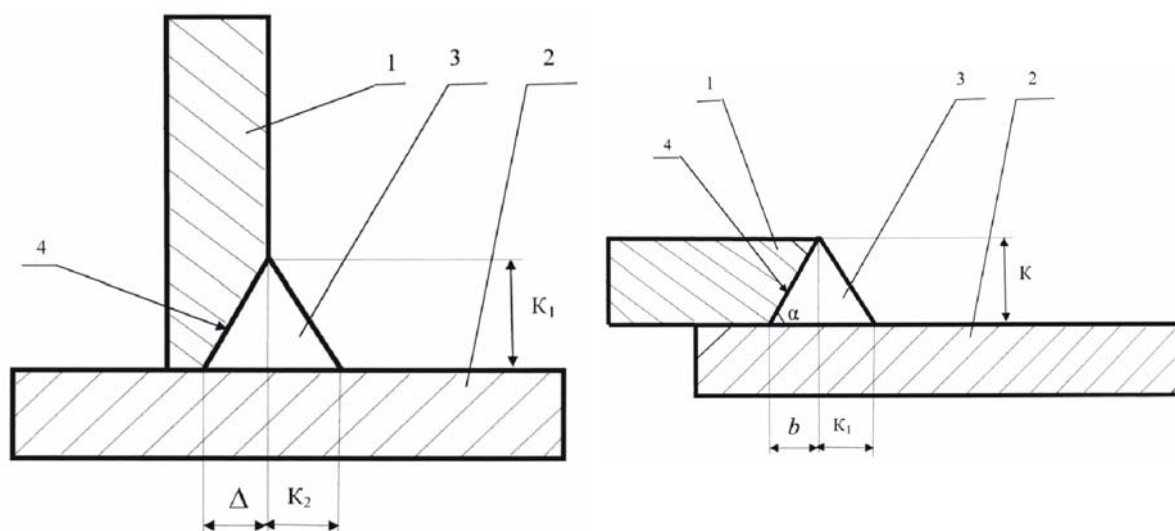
Схема таврового (а) и нахлесточного (б) сварного соединения:
